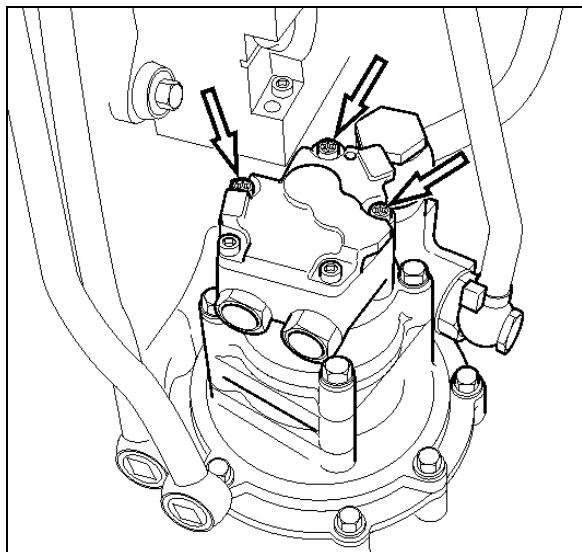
DÉPOSE DE LA POMPE À CARBURANT
